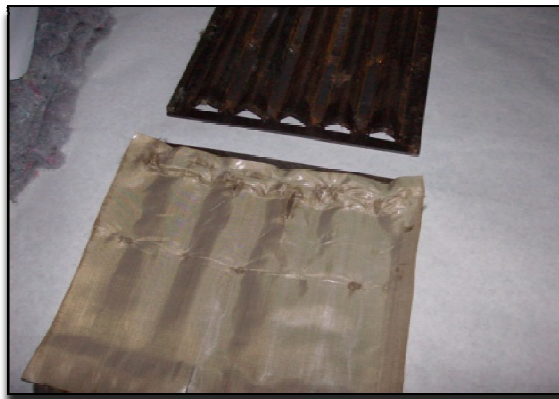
8 Conjunto de moldes macho/fêmea
